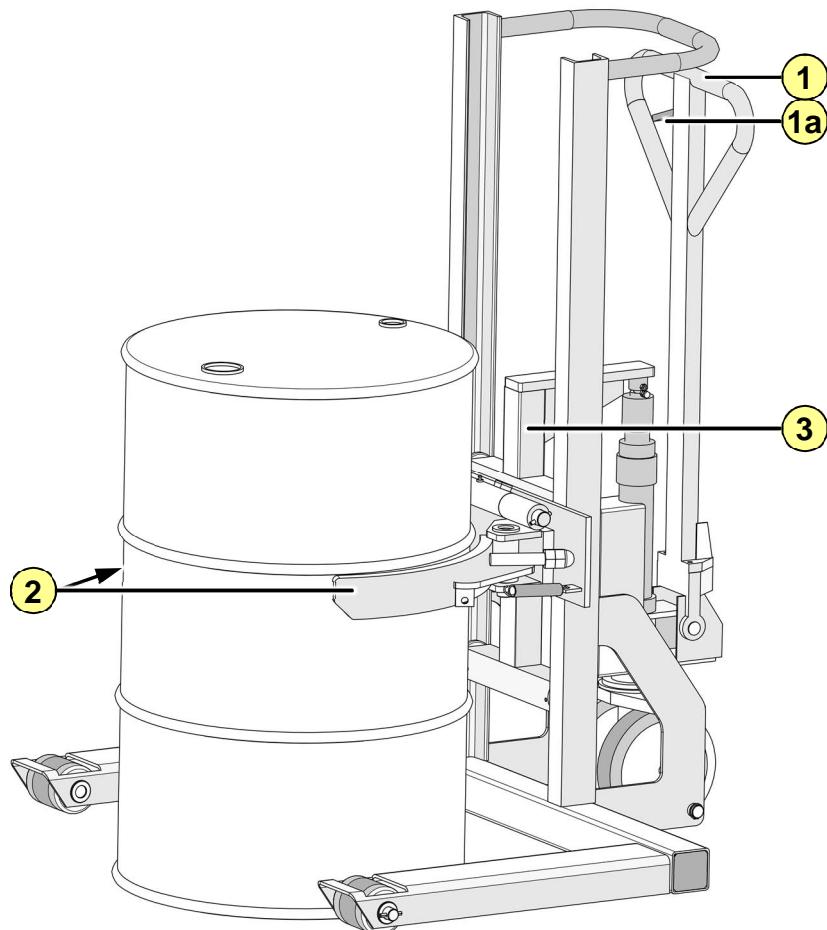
Baugruppen Fassheberoller, Typ FHR 600 K
